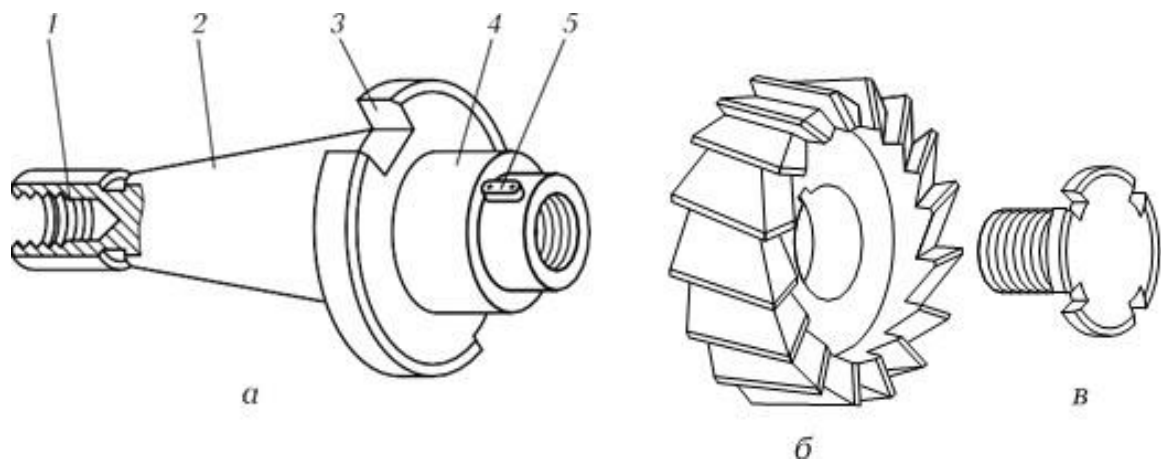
Концевая оправка (а), торцовая насадная фреза (б) и крепежный винт (в):
